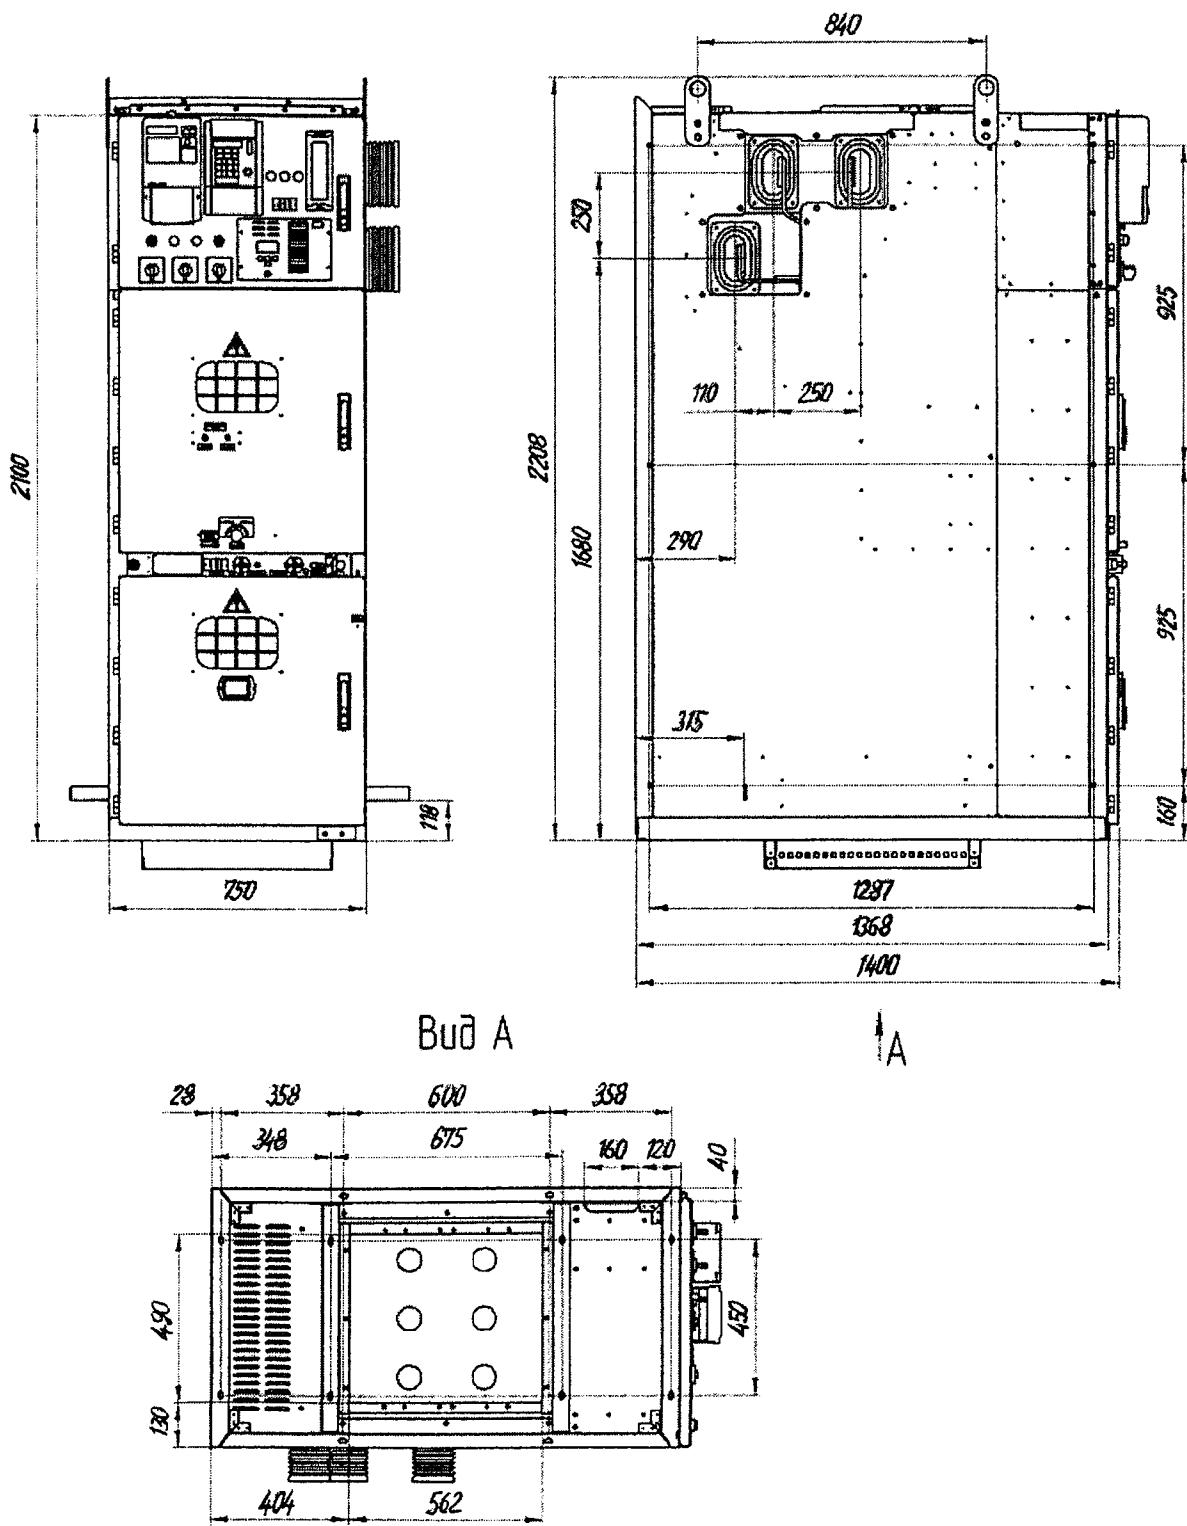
Габаритные и присоединительные размеры шкафа КРУ «ТЕМЗА» на номинальный ток 1600-2000 А
